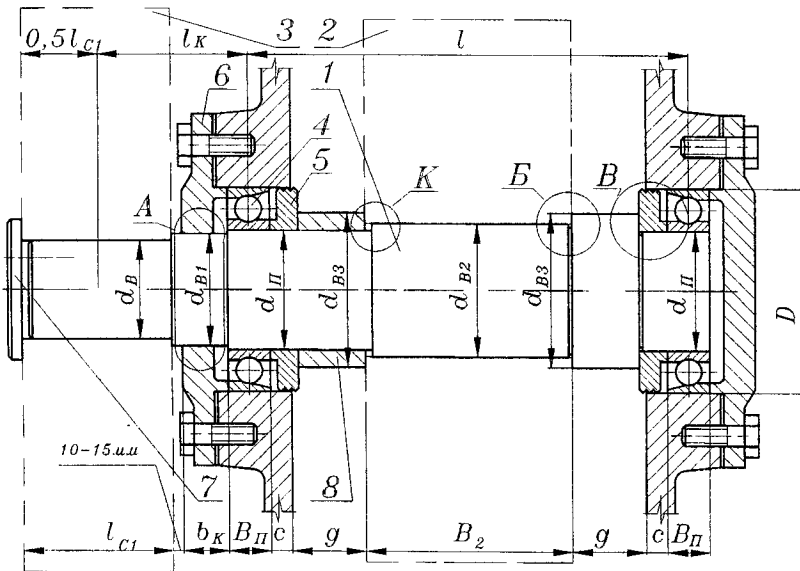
Ведений вал закритої косозубої циліндричної або черв'ячної передачі
